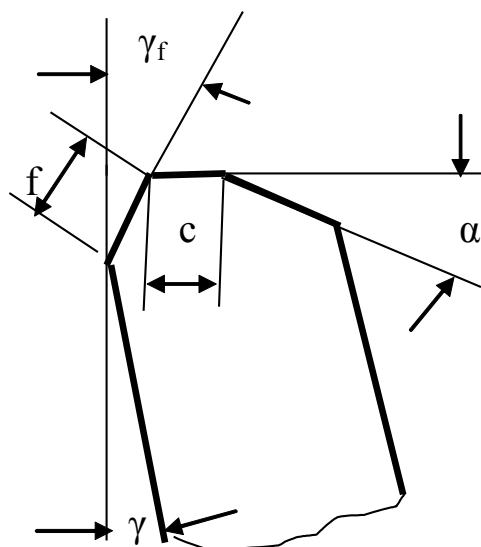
Рекомендуемая форма режущего клина концевых фрез:
